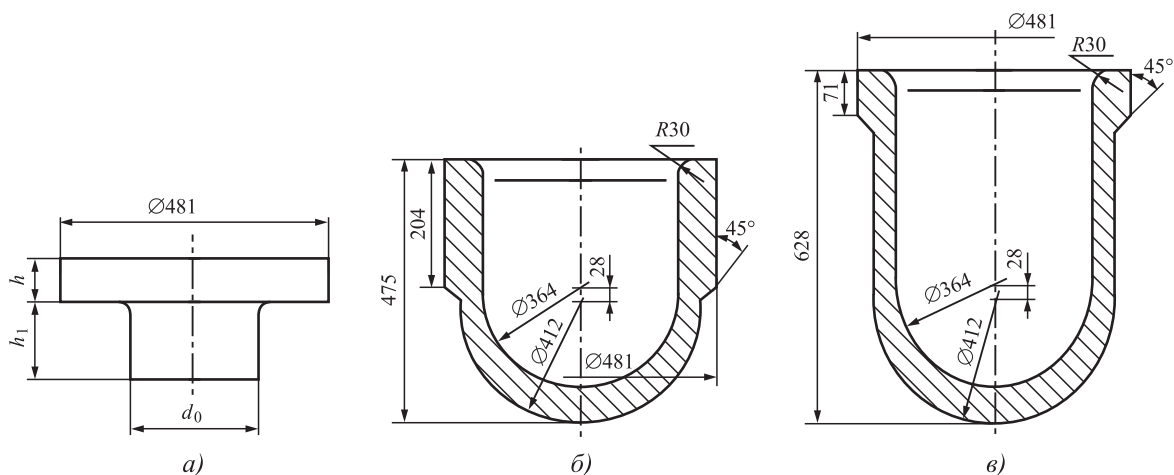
Ступенчатая заготовка для выдавливания (а) и два перехода (б, в) ее формоизменения штамповкой
